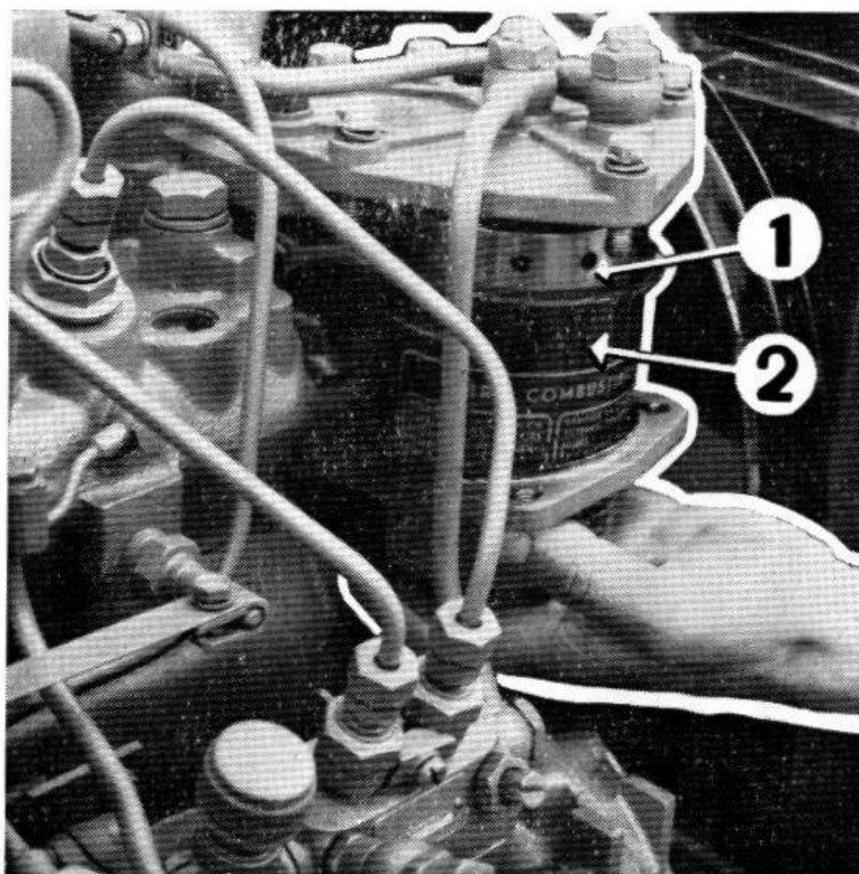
Montage de la cartouche du filtre à combustible.
